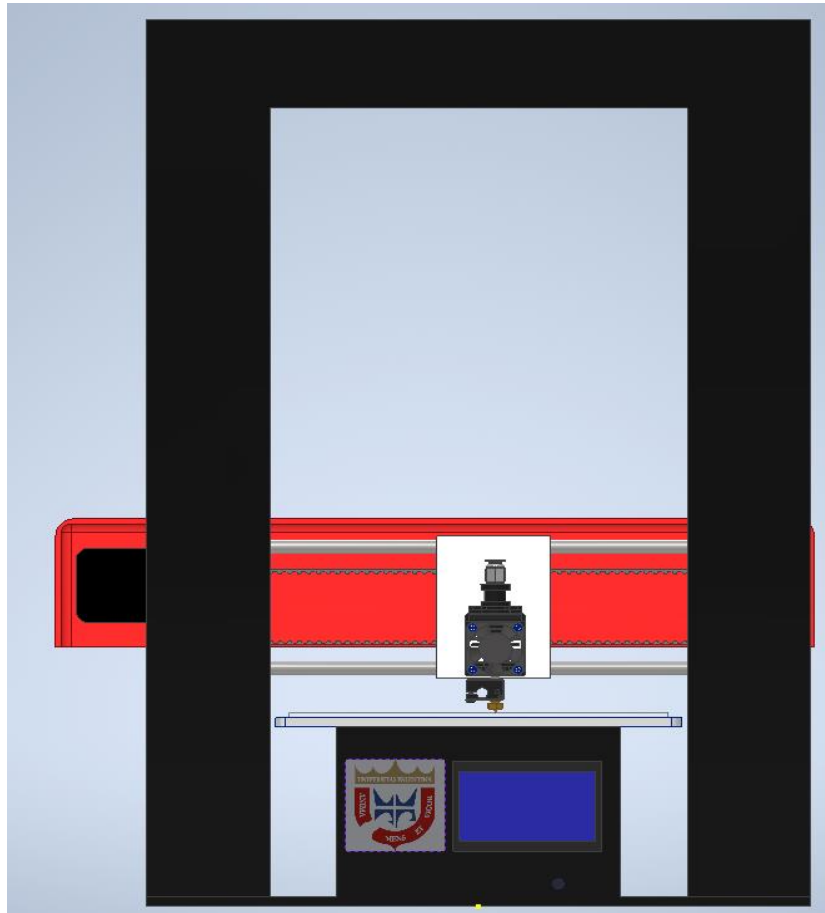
Vista frontal del ensamblaje final de la impresora 3D diseñada
